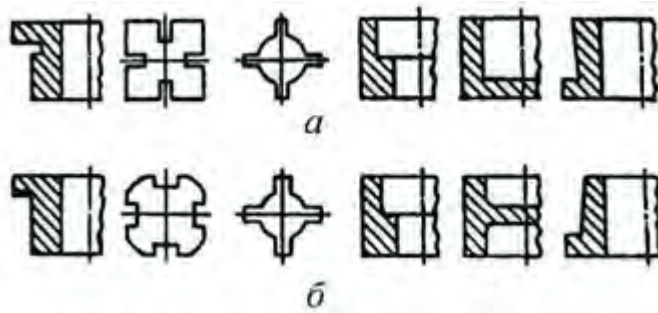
Приклади конструкцій заготовок із порошкових матеріалів:
